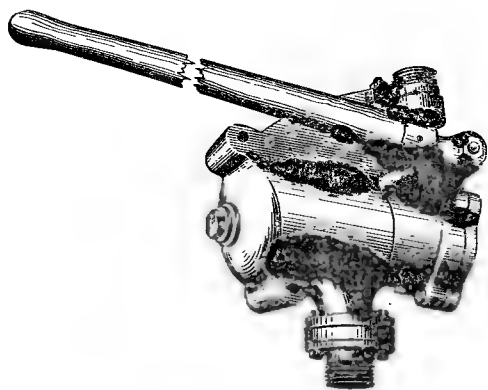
Общий вид ручного поршневого насоса двойного действия.
